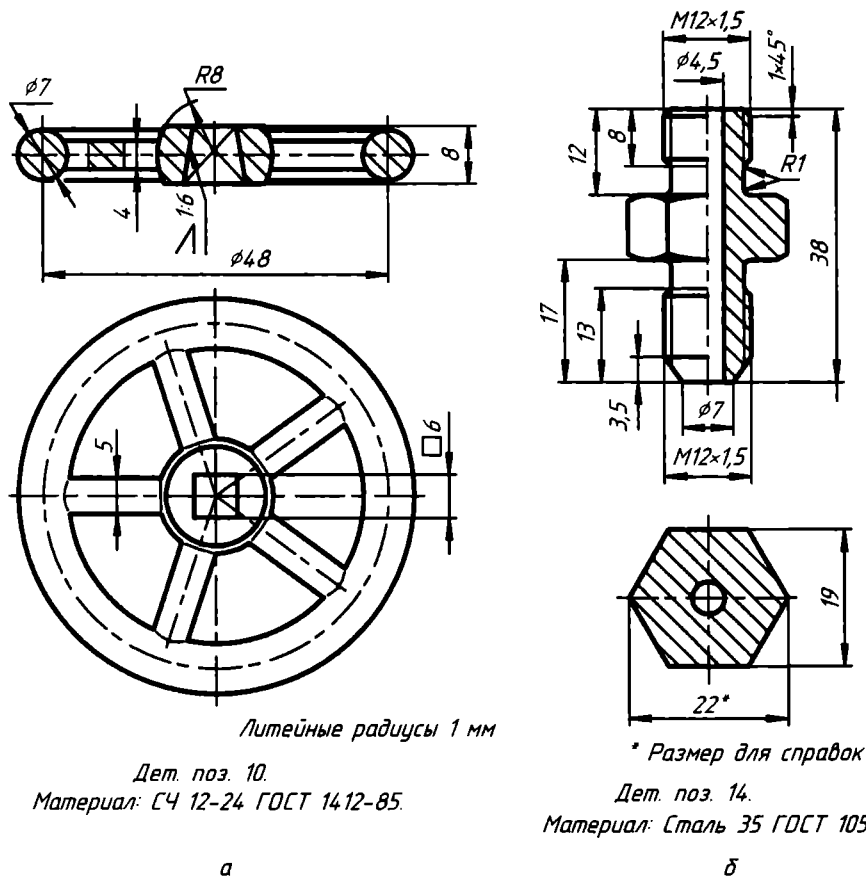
Чертежи: а — маховика; б — штуцера
